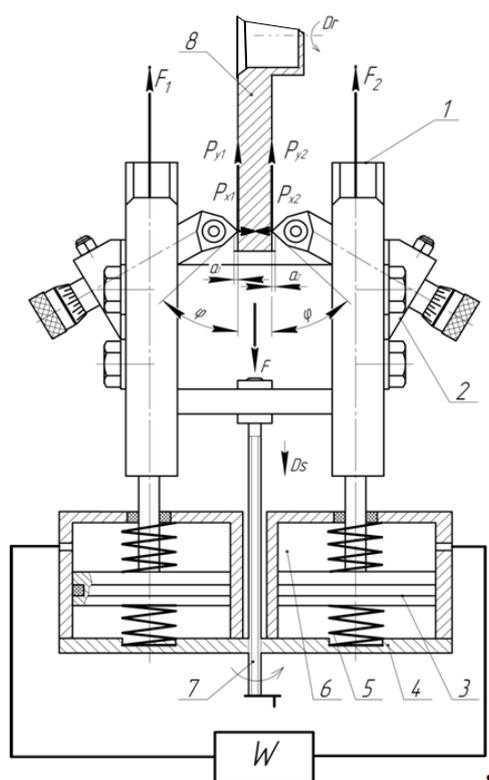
Схема разработанного модуля для двурезцовой обработки рабочих поверхностей тормозного диска: 1 - направляющая резцедержателя; 2 - резцедержатель; 3 - поршень; 4 - корпус; 5 - пружина; 6 - полость с маслом; 7 - винт подачи; 8 - тормозной диск.
